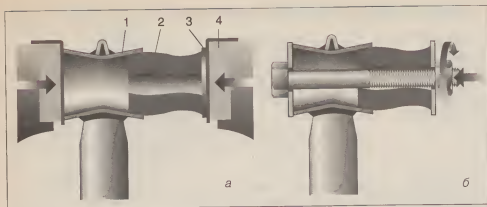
Установка в проушину резиновой втулки: а – в тисках; б – с помощью болта; 1 – проушина; 2 – втулка; 3 – шайба; 4 – тиски.
